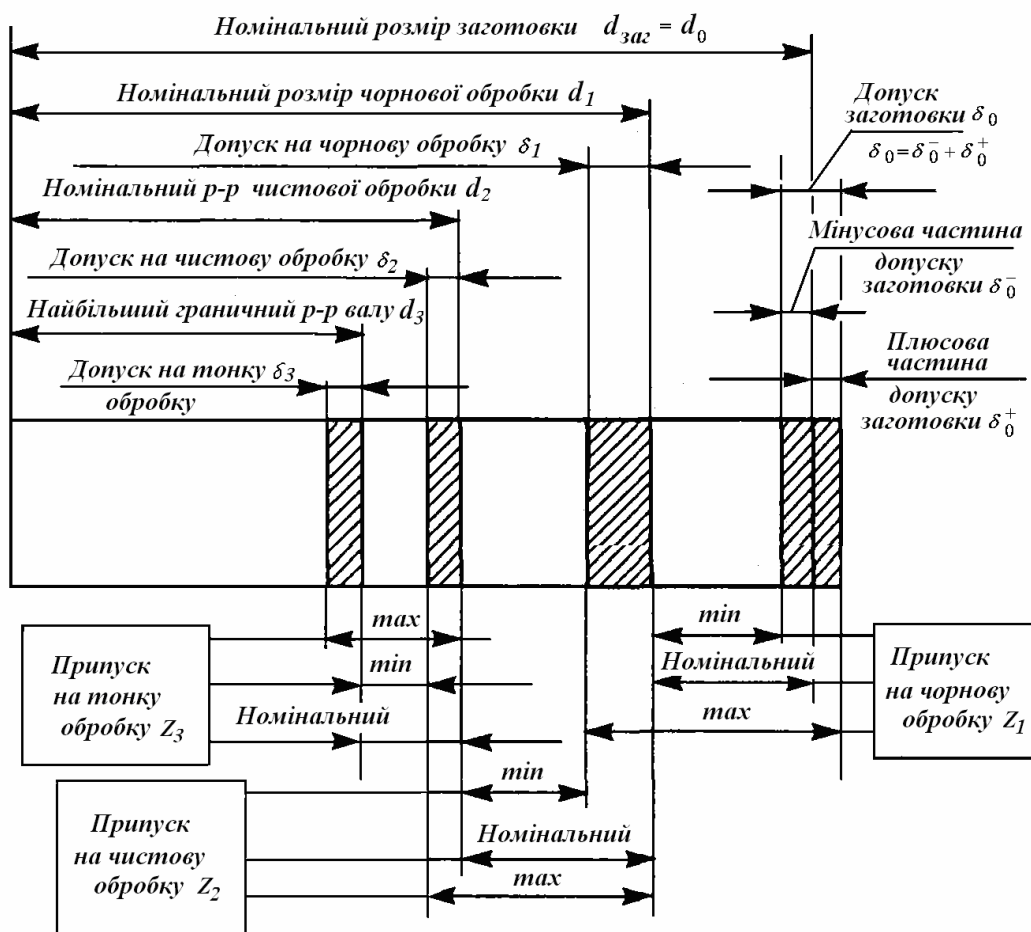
Схема розташування операційних припусків і допусків на різних стадіях обробки для зовнішніх поверхонь (валів)
